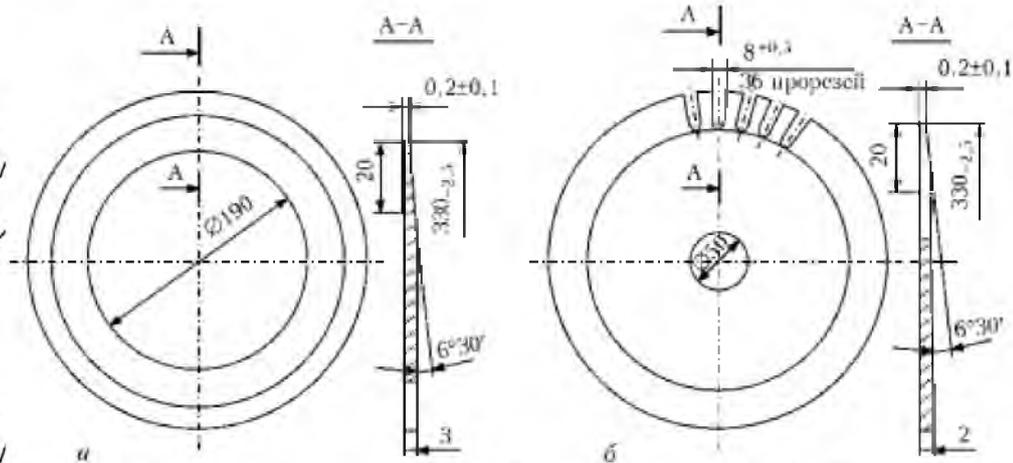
Дискові ножі, наплавлені твердим порошкоподібним сплавом електроконтактним способом для приварювання стрічки до диска лущильника
